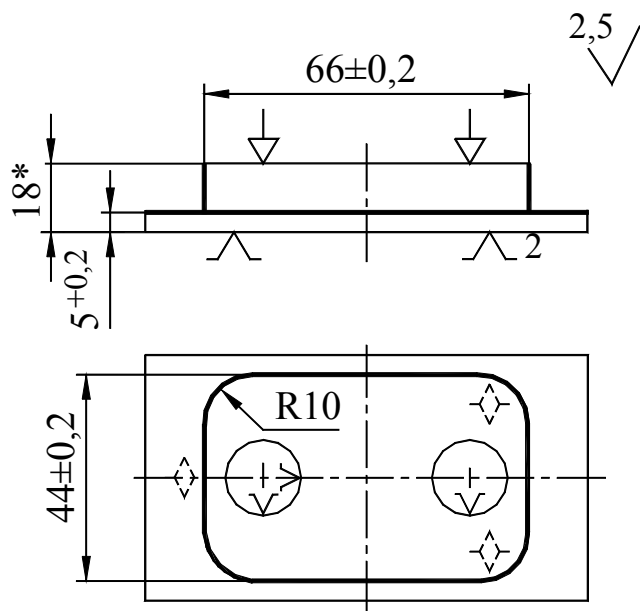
Операционный эскиз операции фрезерной с ЧПУ
